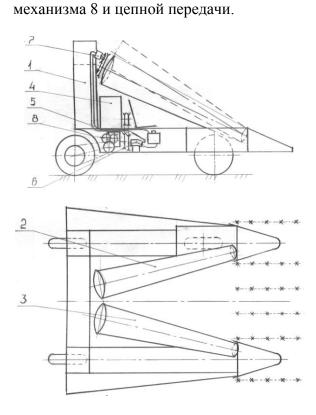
Схема самоходной экспериментальной установки для поднятия стеблей рапса: 1 – рама; 2 – конус делительный левый; 3 – конус делительный правый; 4 – двигатель; 5 – редуктор; 6 – насос регулируемой производительности;
